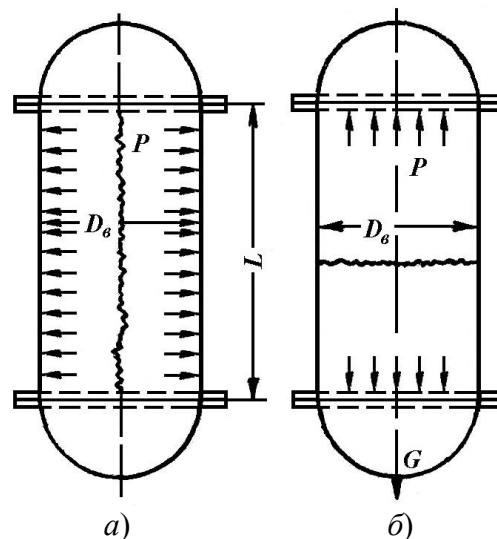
Схеми розподілу зусиль до розрахунку товщини циліндричного корпусу теплообмінника:
